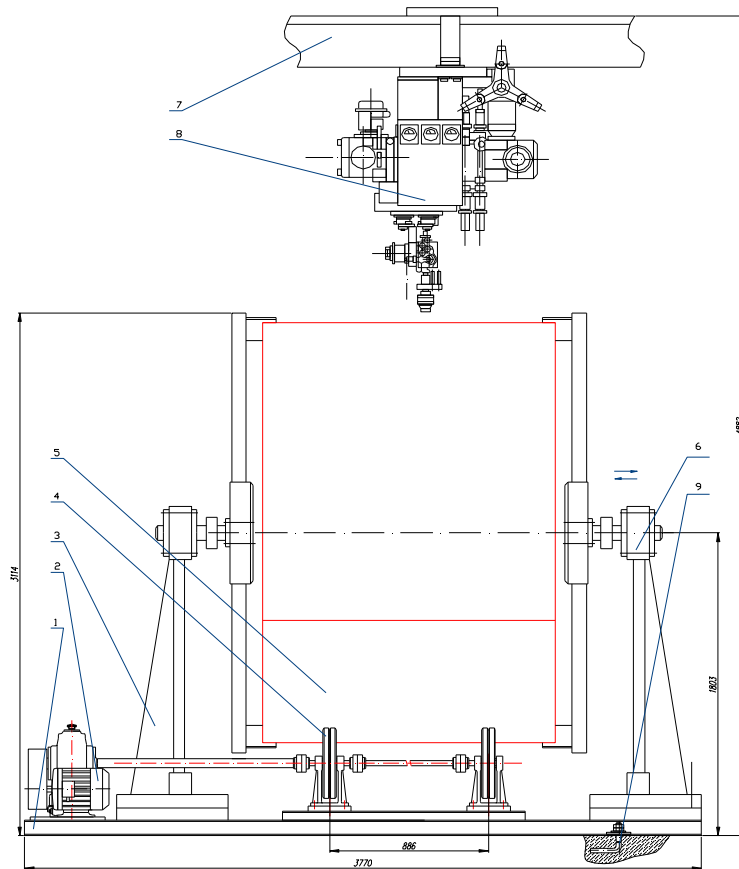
Эскиз установки для сварки продольного шва обечайки.
